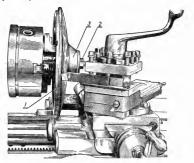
Приспособление для заточки лезвий дисков: 1 — диси приспособления с хвостовиком; 2 — гайна; 3 — шайба.
